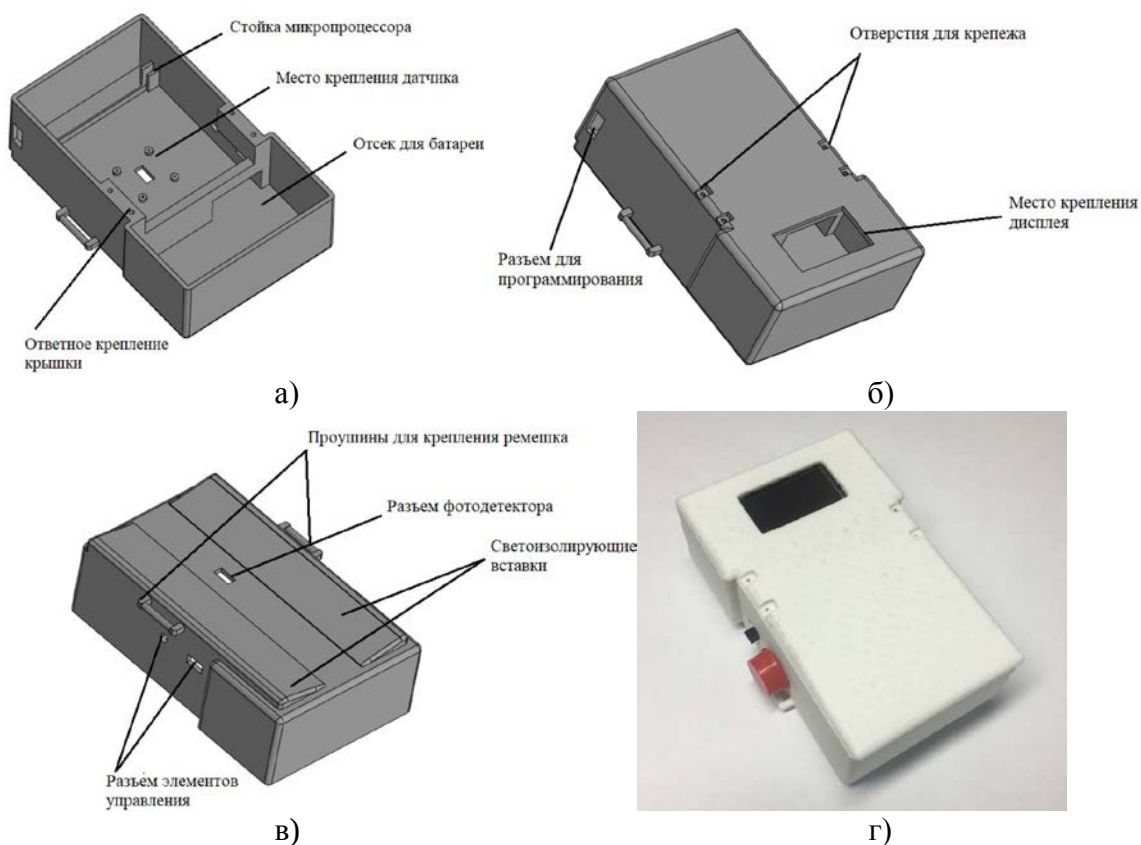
а) внутренний вид корпуса; б) общий вид корпуса; в) нижний вид корпуса; г) вид прибора в сборе
